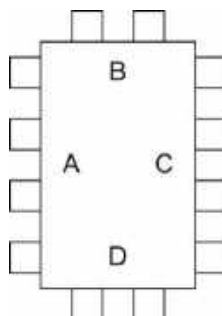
Схема расположения вводов или отверстий в корпусе ПКВ ОП-П-XXX... X
